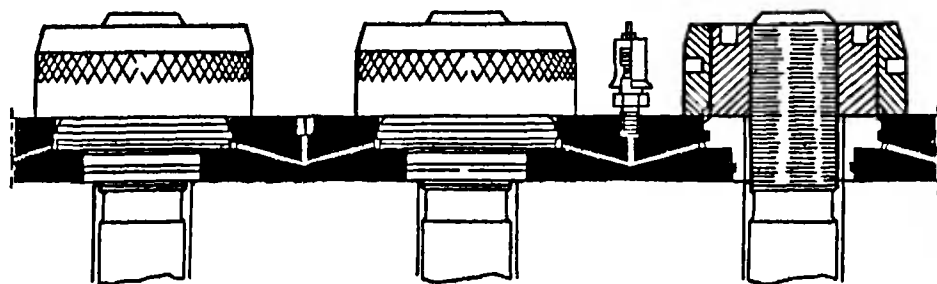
Гидравлическое кольцо, устанавливаемое на крышку цилиндра для быстрой и равномерной затяжки шпилек на двигателе типа К90GF.
